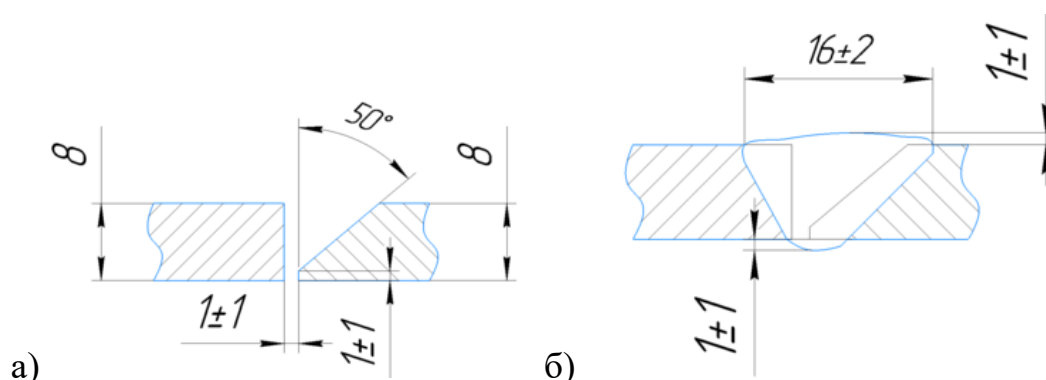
Сборка(а) и Сварка(б) соединения №5
